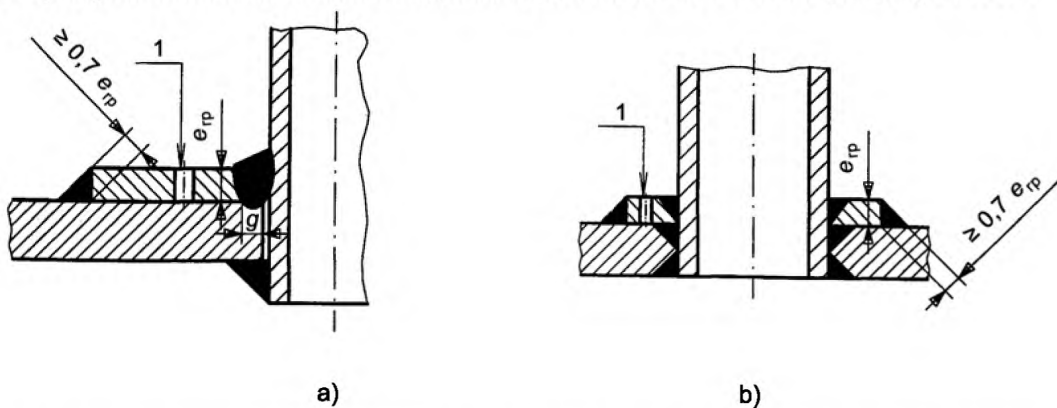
, лист 1 – Типовые сварные соединения для плоских днищ и фланцев
